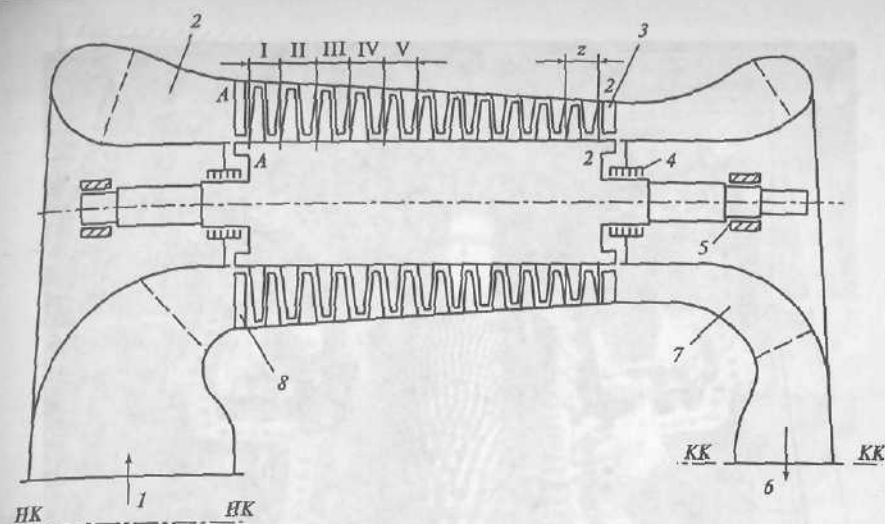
Конструктивная схема осевого компрессора ГТУ
